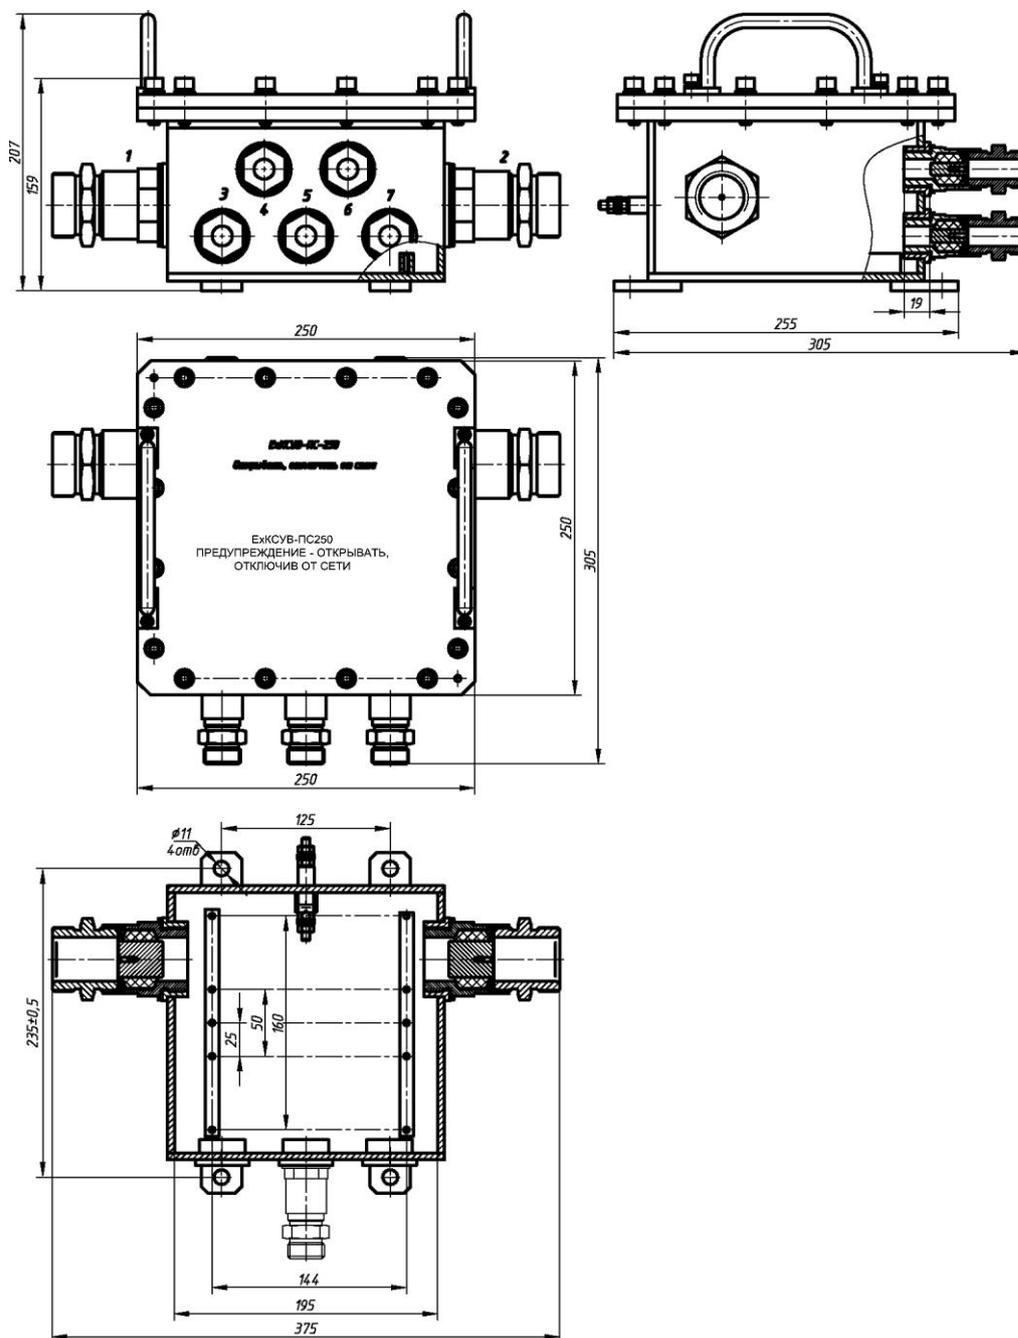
Габаритный чертеж коробки ЕхКСУВ-ПС250.
